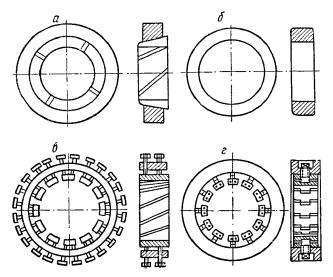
Кольца для прессовки комплекта пластин коллектора: a, δ — для прессовки под прессом; ϵ , ϵ — для прессовки болтами.
